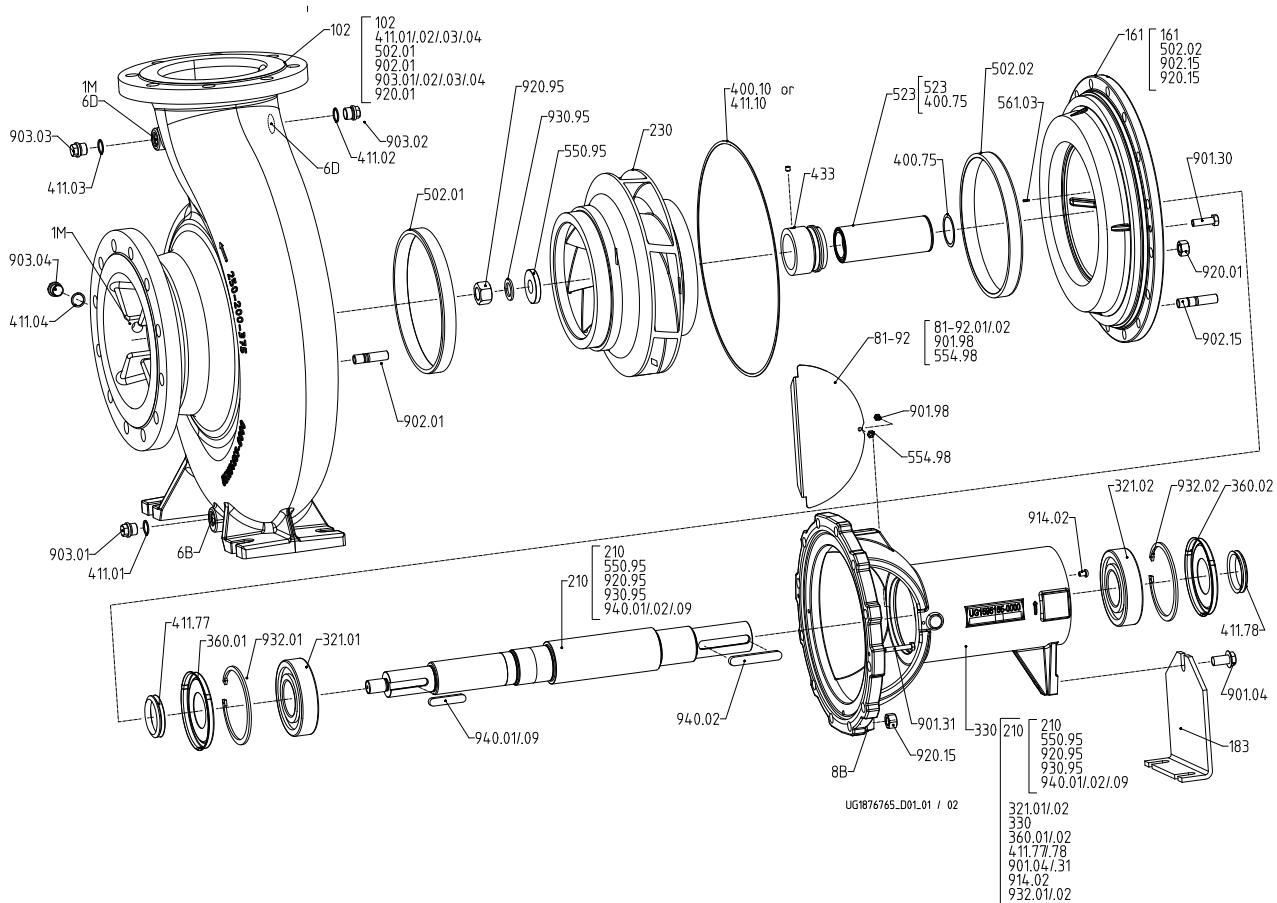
Исполнение со стандартным торцевым уплотнением и привинчиваемой крышкой корпуса
